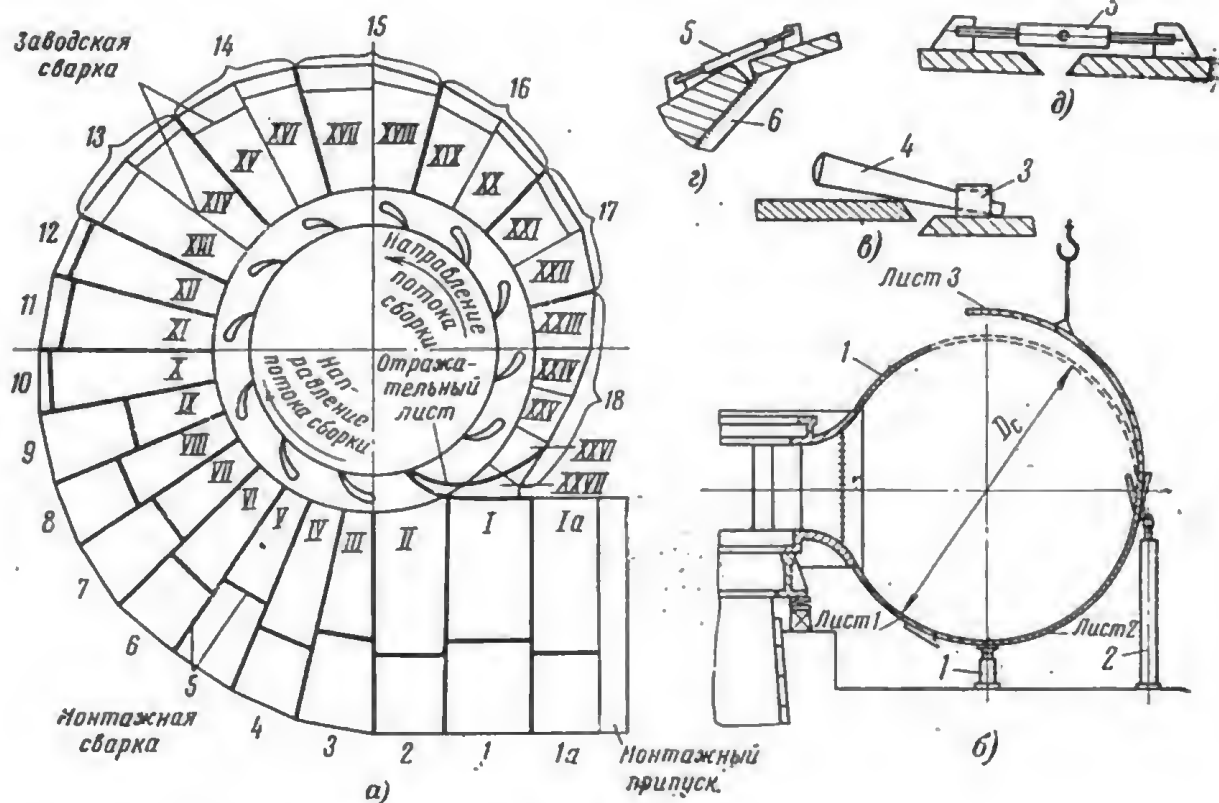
Сборочная схема сварной спиральной камеры.
